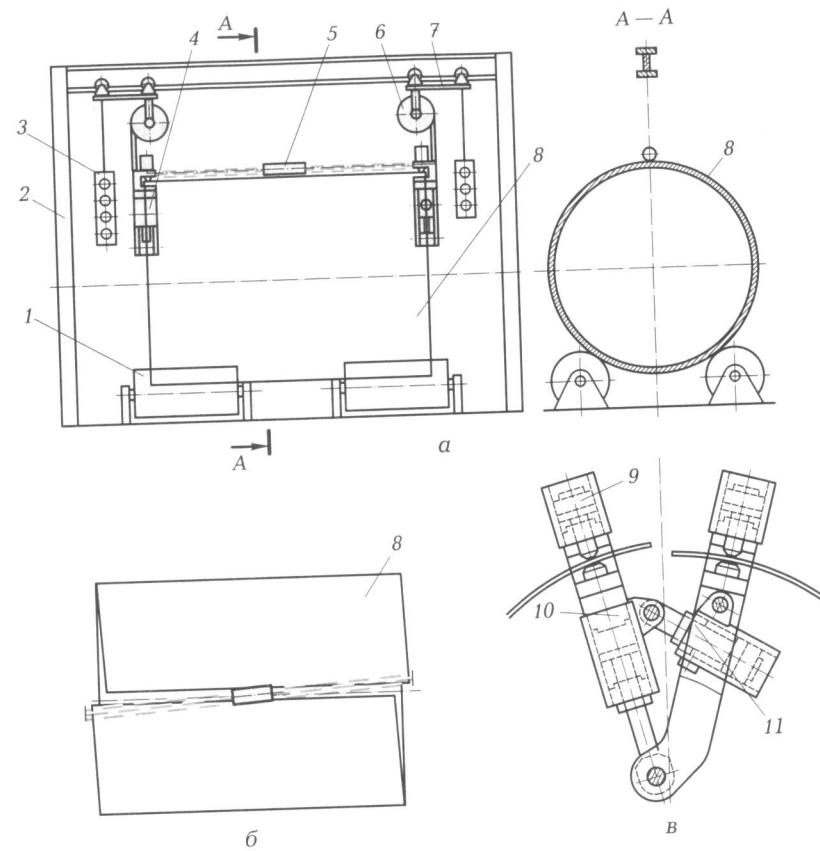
Установка для сборки обечайек по продольным стыкам:
